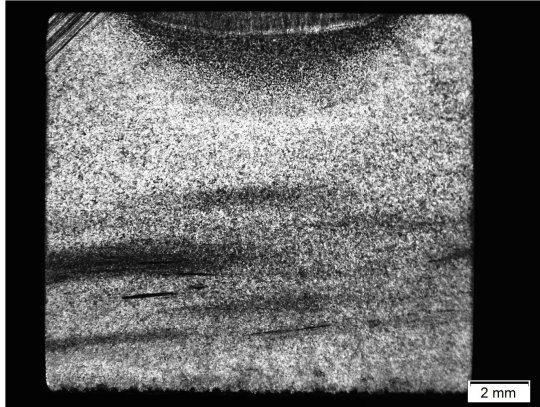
Probe G01-02, Schweißnaht FAT 90, Riss in der Schweißnaht, Detail Rissbeginn und Kerbe [78]
